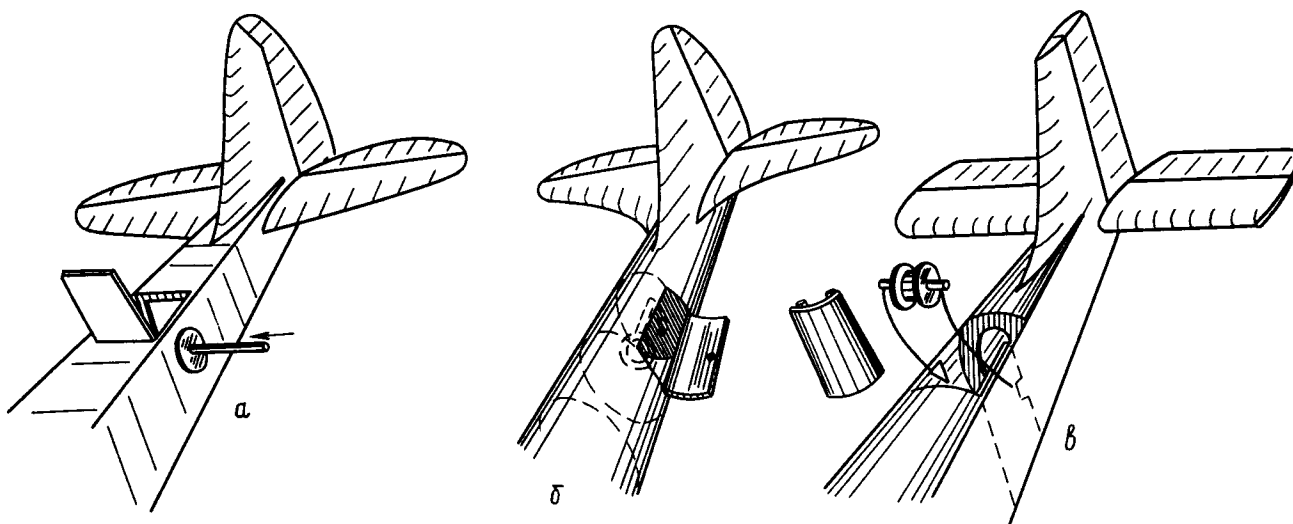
Способы крепления резинового шнура в хвостовой части фюзеляжа:
